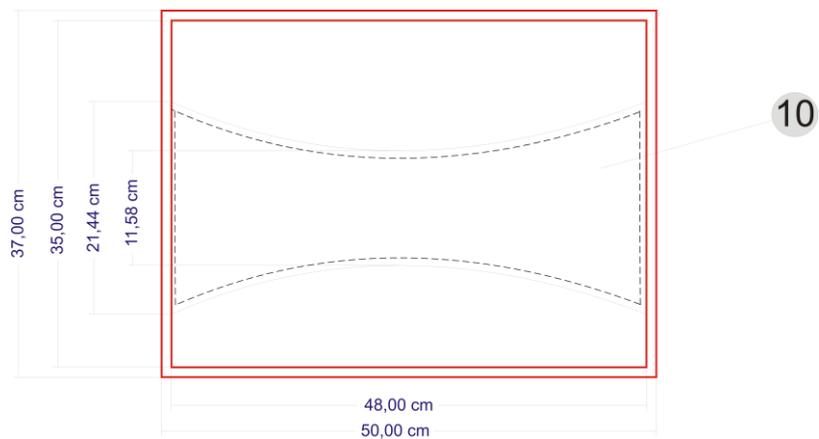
Desenho Técnico - Vista Interna da Tampa
